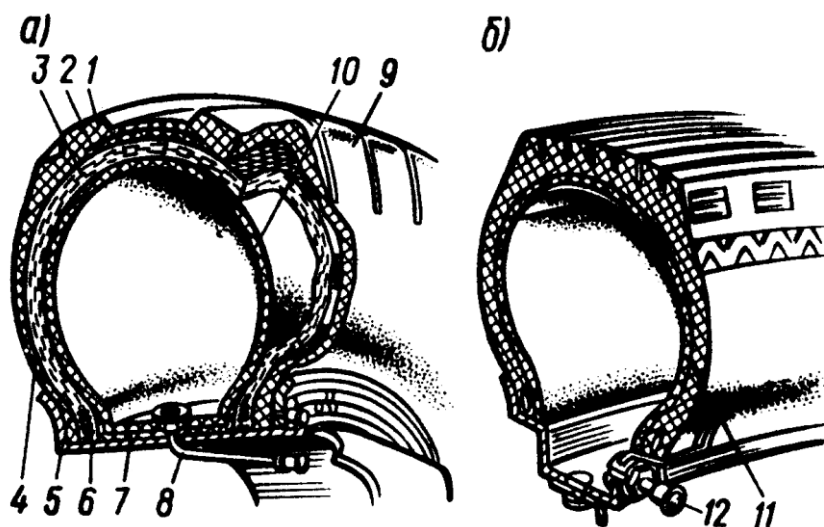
Основные части пневматической шины: 1 – протектор, 2 – подушечный слой (брекер), 3 – каркас, 4 – боковина, 5 – борт, 6 – кольцо-сердечник, 7 – ободная лента, 8 – вентиль, 9 – покрышка, 10 – камера, 11 – специальный герметизирующий слой, 12 – вентиль
